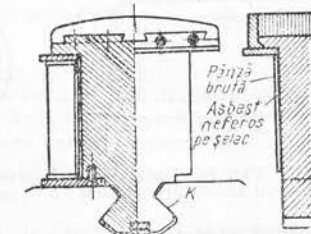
Pol masiv și piesă polară executată din tole prinse prin coadă de rândunică cu fixare inferioară cu pene.
